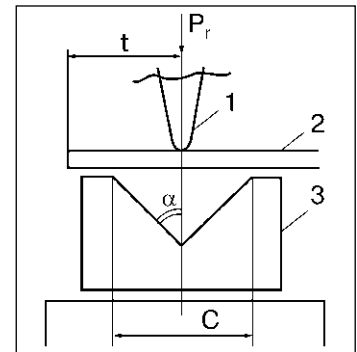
Схема гибки листовой стали на кромко-гибочных прессах: 1 — верхний штамп; 2 — заготовка; 3 — нижний штамп
